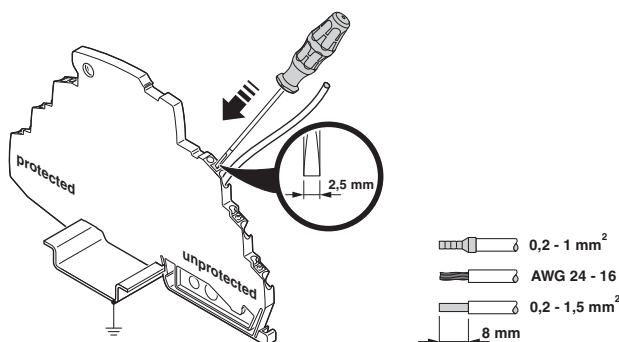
Variante di collegamento connessione Push-in (larghezza costruttiva 3,5 mm)
